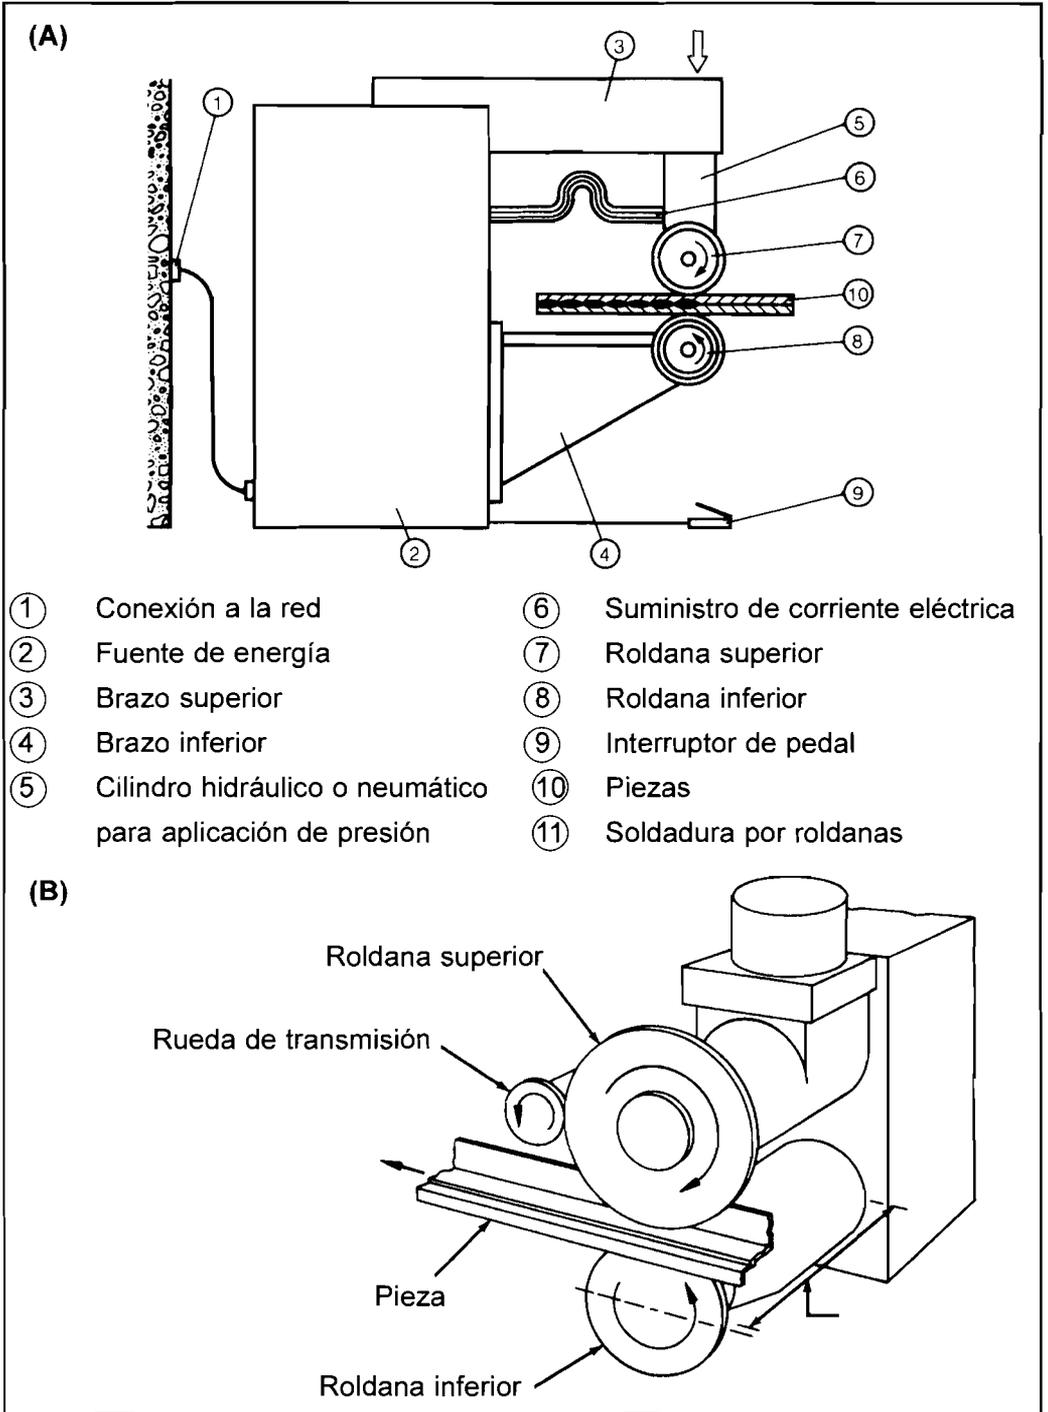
(A) MÁQUINA DE SOLDEO POR ROLDANAS. (B) DETALLE DE LAS ROLDANAS
